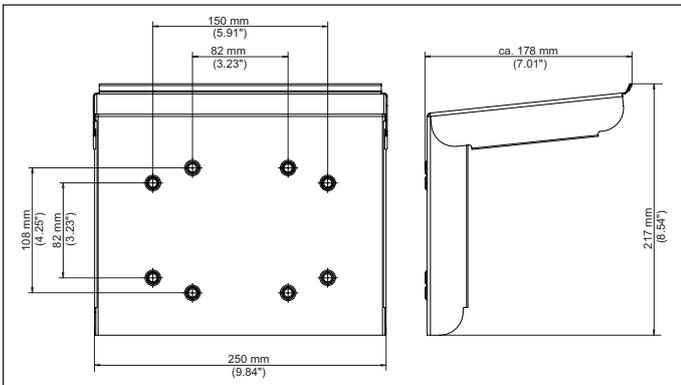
Dimensiones protección solar VEGAMET 861, 862
